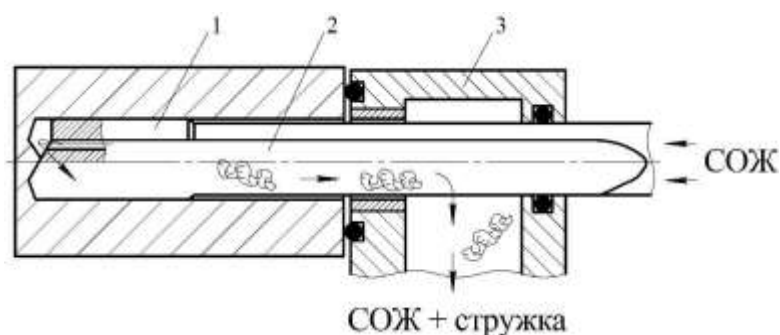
Схема сверления глубокого отверстия ружейным сверлом:
